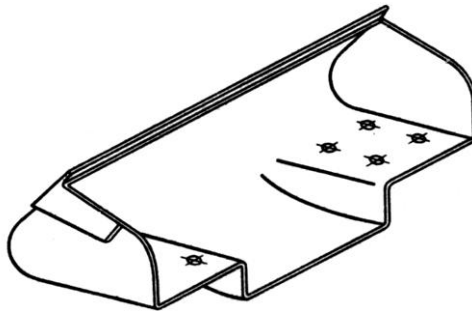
Конструкція ковша з заглибленою задньою стінкою
